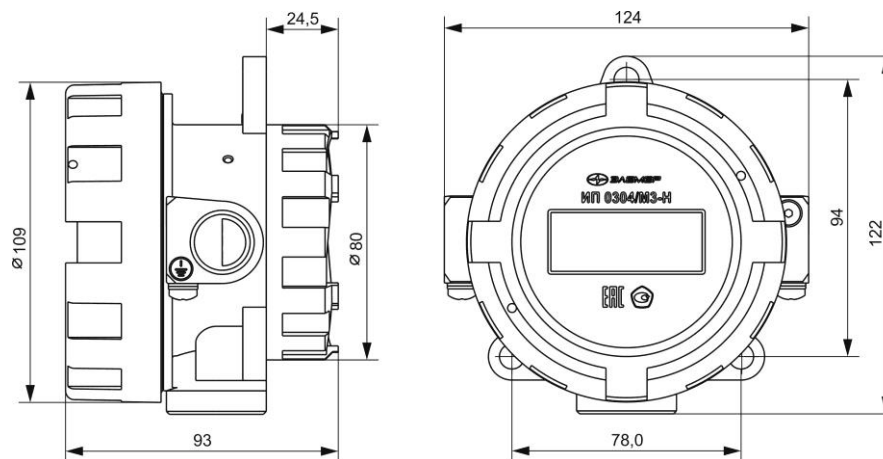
Габаритные размеры ИП 0304/М3-Н-АГ18
